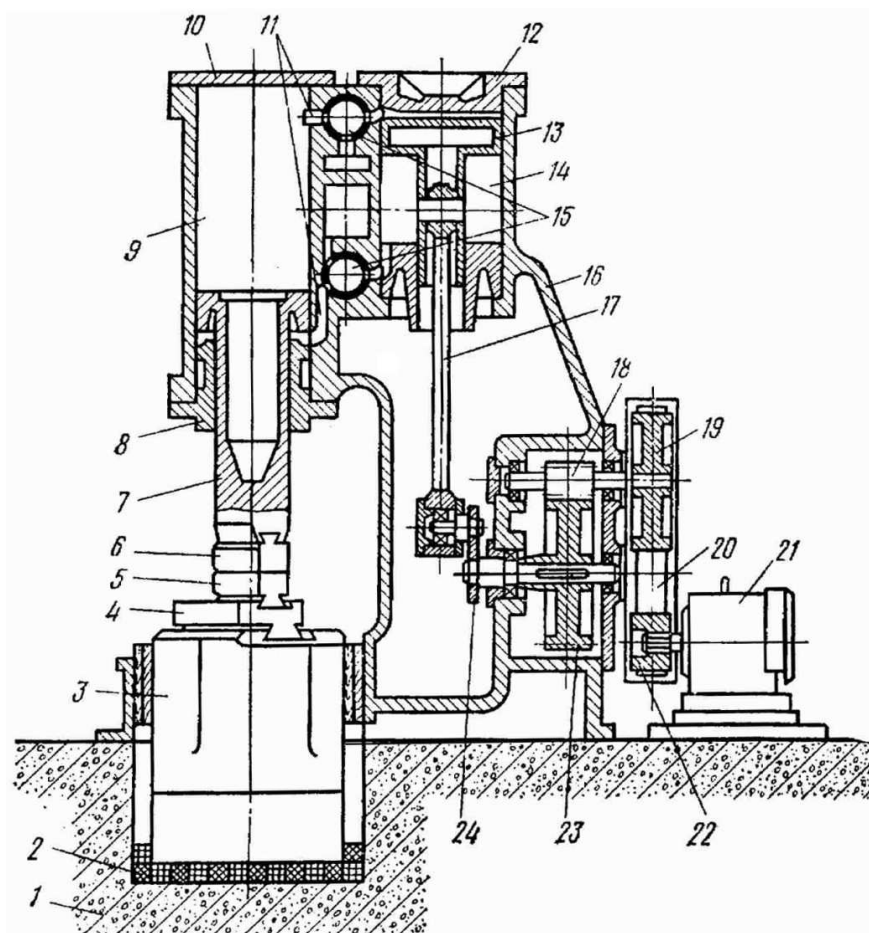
Схема пневматического двухцилиндрового одностоечного ковочного молота: 1 – фундамент; 2 – деревянные брусья; 3 – шабот; 4 – промежуточная подушка; 5 – нижний боек; 6 – верхний боек; 7 – баба; 8 – нижняя крышка рабочего цилиндра; 9 – рабочий цилиндр; 10 – верхняя крышка рабочего цилиндра; 11 – каналы; 12 – верхняя крышка компрессорного цилиндра; 13 – поршень компрессорного цилиндра; 14 – компрессорный цилиндр; 15 – распределительные краны; 16 – станина; 17 – шатун; 18 и 23 – зубчатые колеса; 19 – маховик; 20 – ремень плоский; 21 – электродвигатель; 22 – шкив; 24 – кривошип
